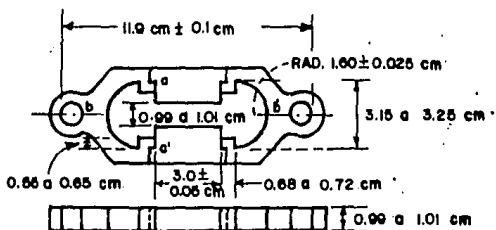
MOLDE DE LA PRUEBA FUERZA-DUCTILIDAD
